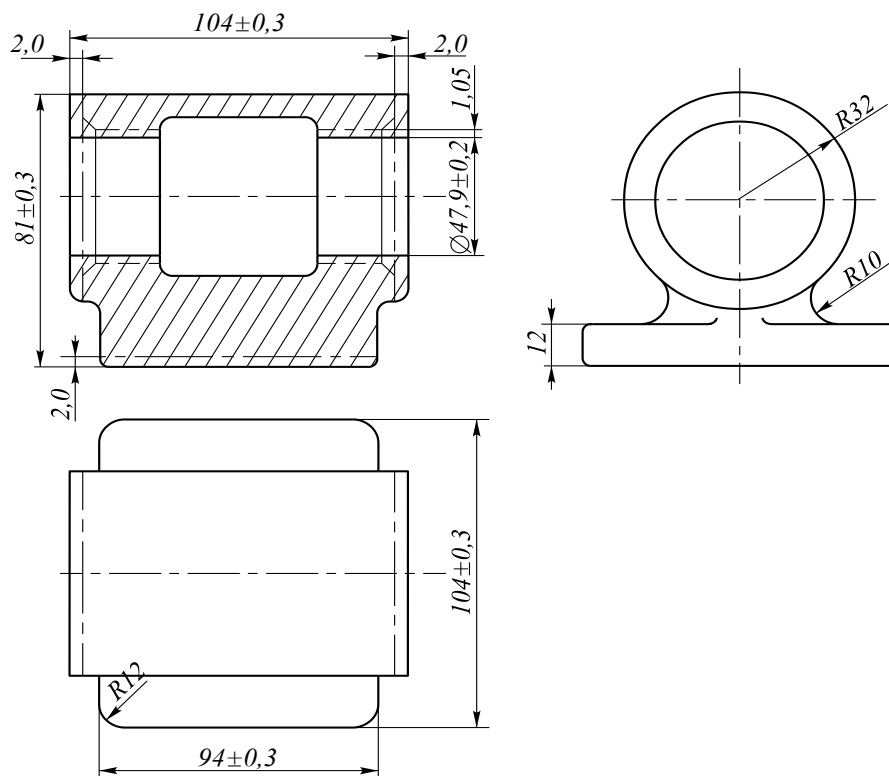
Эскиз заготовки корпуса с начисленными припусками и допусками
